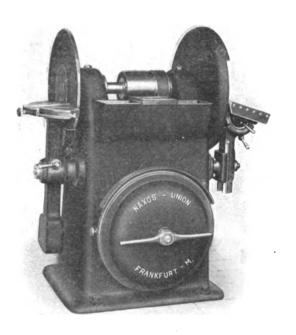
Flächenschleifmaschine mit Stahlscheiben zur Befestigung des Schleifbelages.
